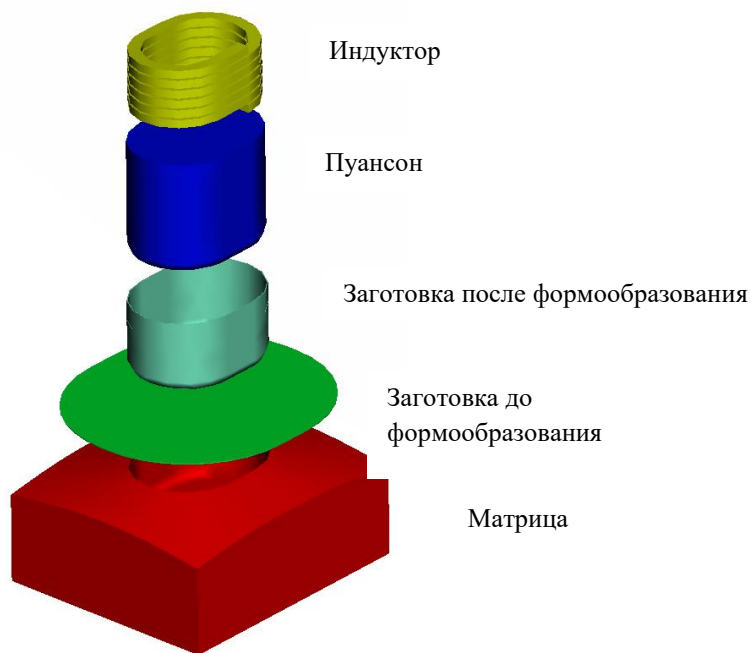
Взаимное расположение заготовки, индуктора и инструмента
